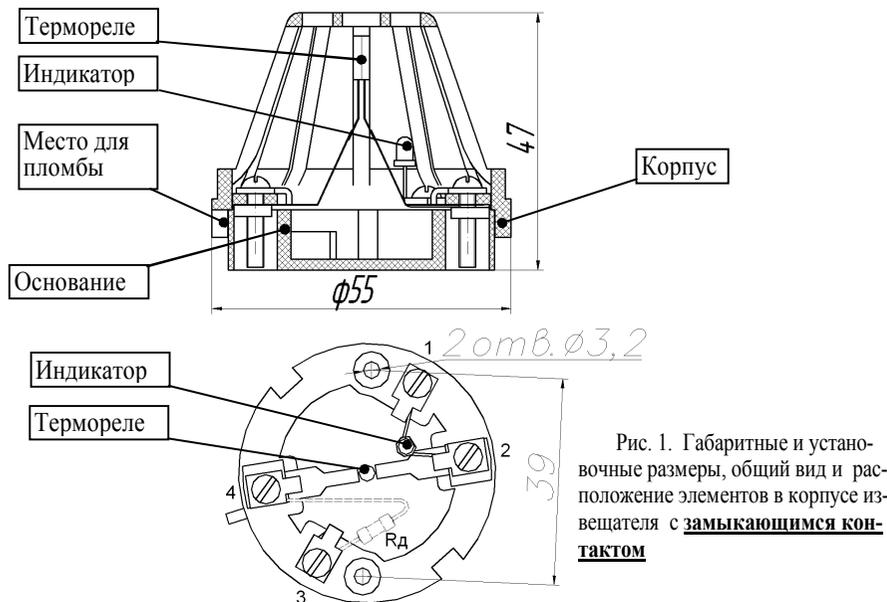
Габаритные и установочные размеры, общий вид и расположение элементов в корпусе извещателя с закрывающимся контактом
